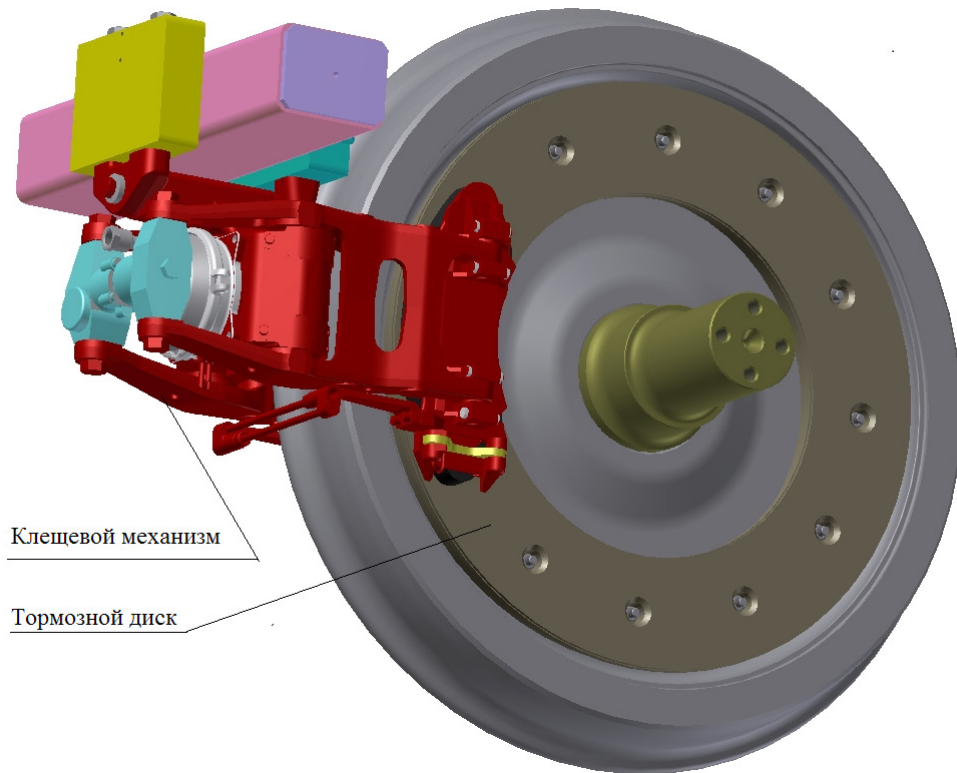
Дисковый тормоз, установленный на ободе колеса
